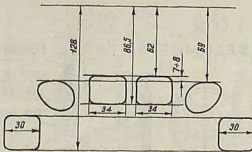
Развертка цилиндра двигателя ИЖ-56, подготовленного для соревнований.
